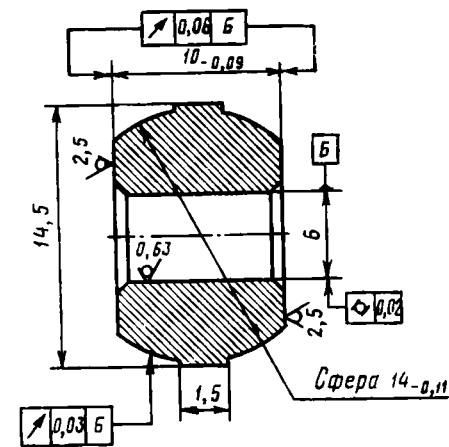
Подшипник скольжения, спрессованный из металлопорошка
